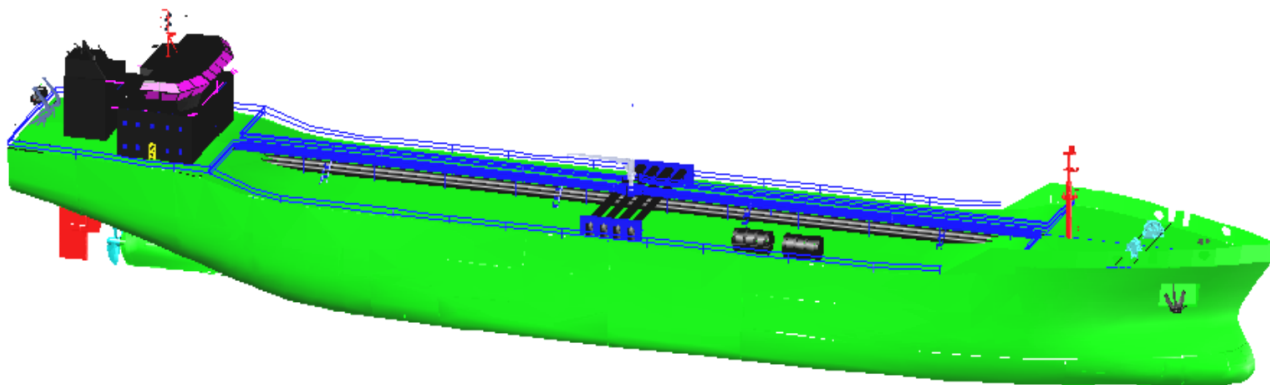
Общий вид корпуса с надстройкой в AutoCAD
